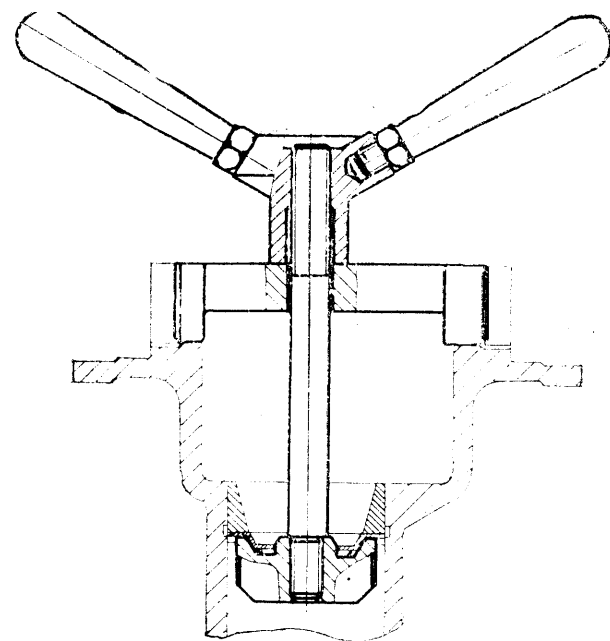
Abziehen des Aussenringes des Kegellagers mit Hilfe der Vorrichtung P 39.
